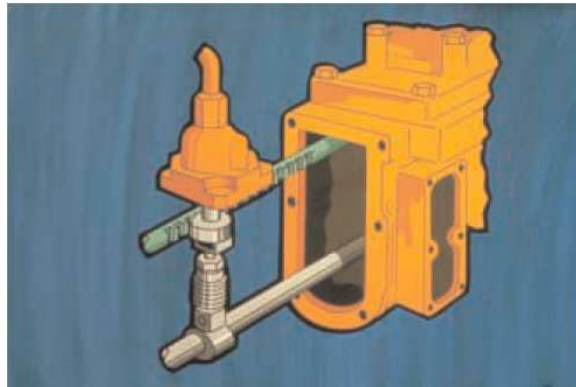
Caja de la bomba de inyección de combustible.
